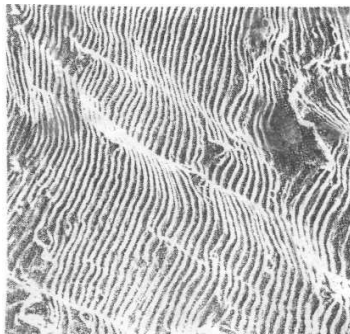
Усталостные бороздки на поверхности излома стали
